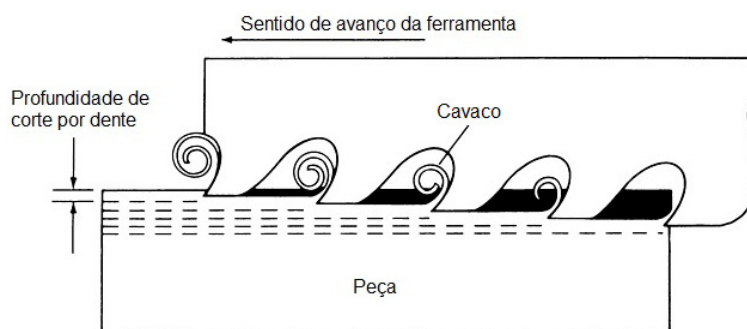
Remoção de material por brochamento de uma superfície plana externa (adaptado de ASM, 1989).
